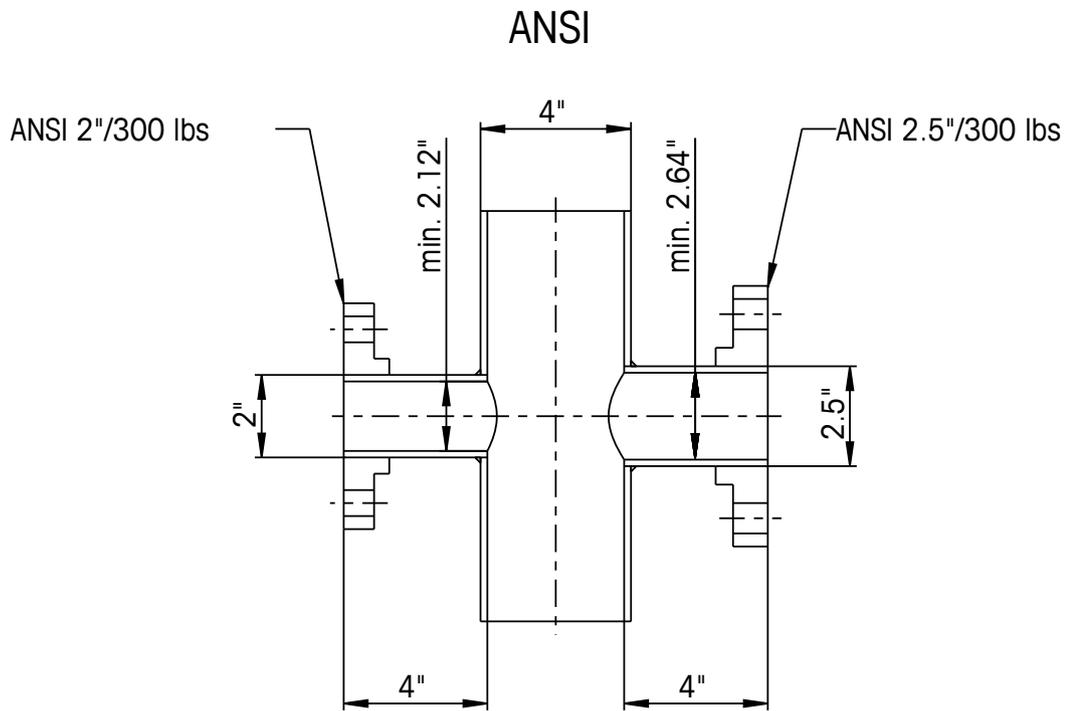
Dimensões recomendadas do flange soldado (para instalações de sondas padrão (SP), sem purga (NP) e com blowback (B))
